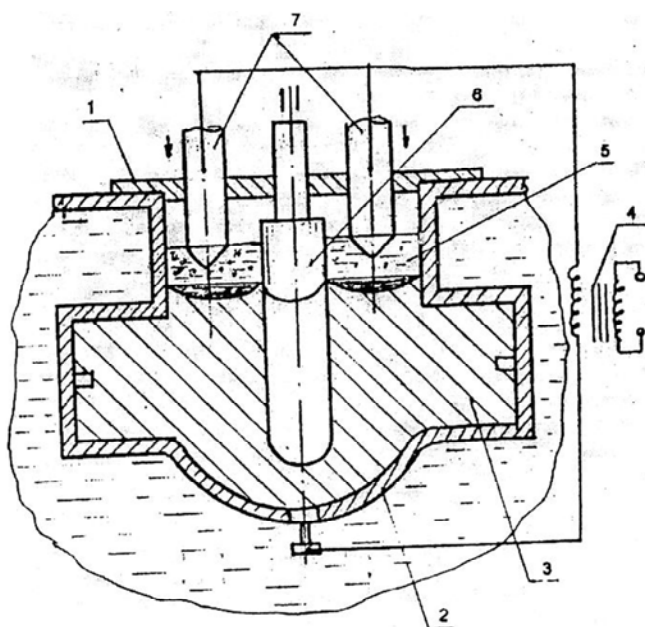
Схема ЭШЛ при формировании отливки в литейной форме:
